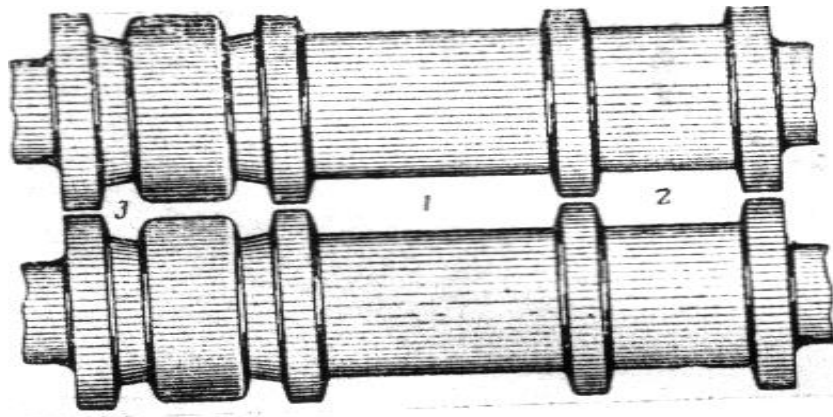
а . Валки і калібри для прокатки балкової заготовки: 1 – бочка; 2 – ребровий калібр; 3 – балковий калібр.
